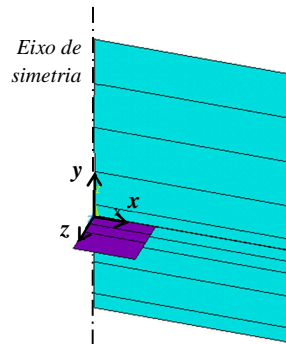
Quinadora e chapa de 1000 mm de comprimento
